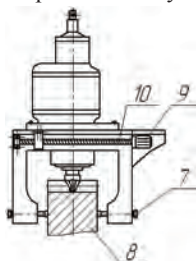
Вид сбоку приставного вертикального зубофрезерного станка
